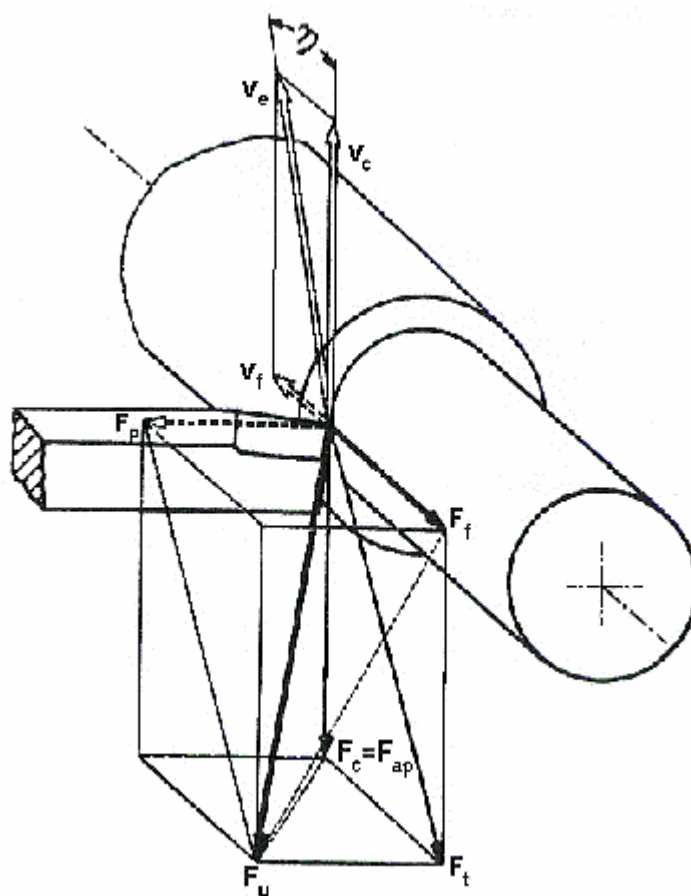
Forças de usinagem e suas diversas componentes na operação de torneamento (Diniz et al, 1999).
